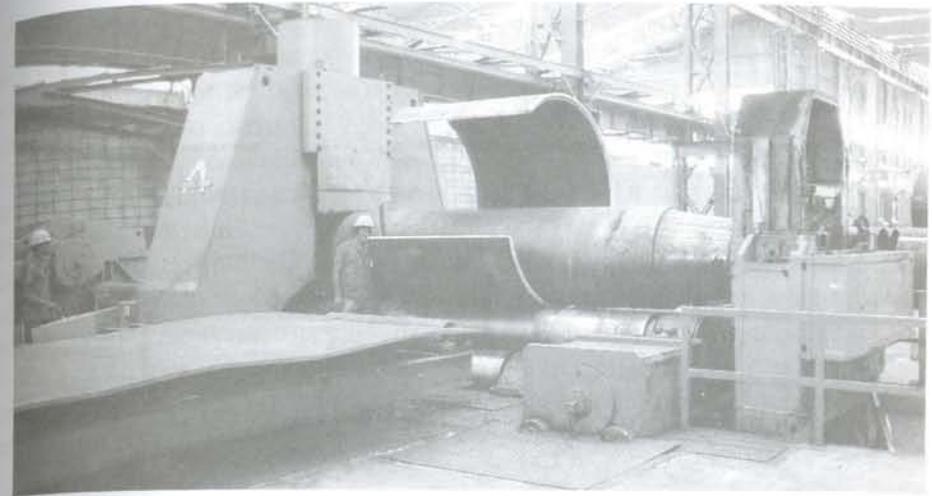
Calandragem de uma chapa. Cortesia de CONFAB Industrial S.A.
